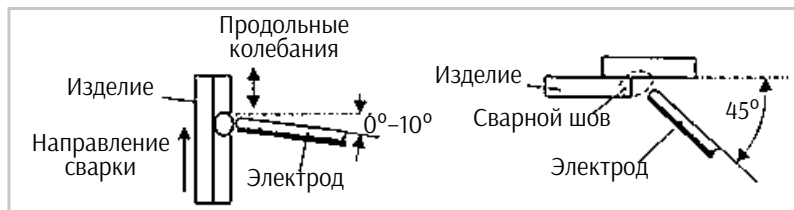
Положение электрода при сварке нахлесточного соединения в вертикальном положении снизу вверх
